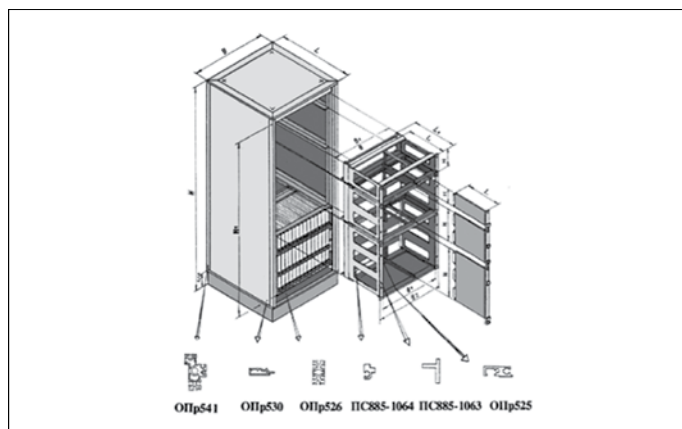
Единый размерный ряд базовых несущих конструкций в системе шкаф-блок-узел
